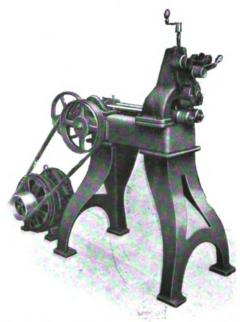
Siederohr-Bearbeitungsmaschine von de Fries & Co., A.-G., Düsseldorf.
